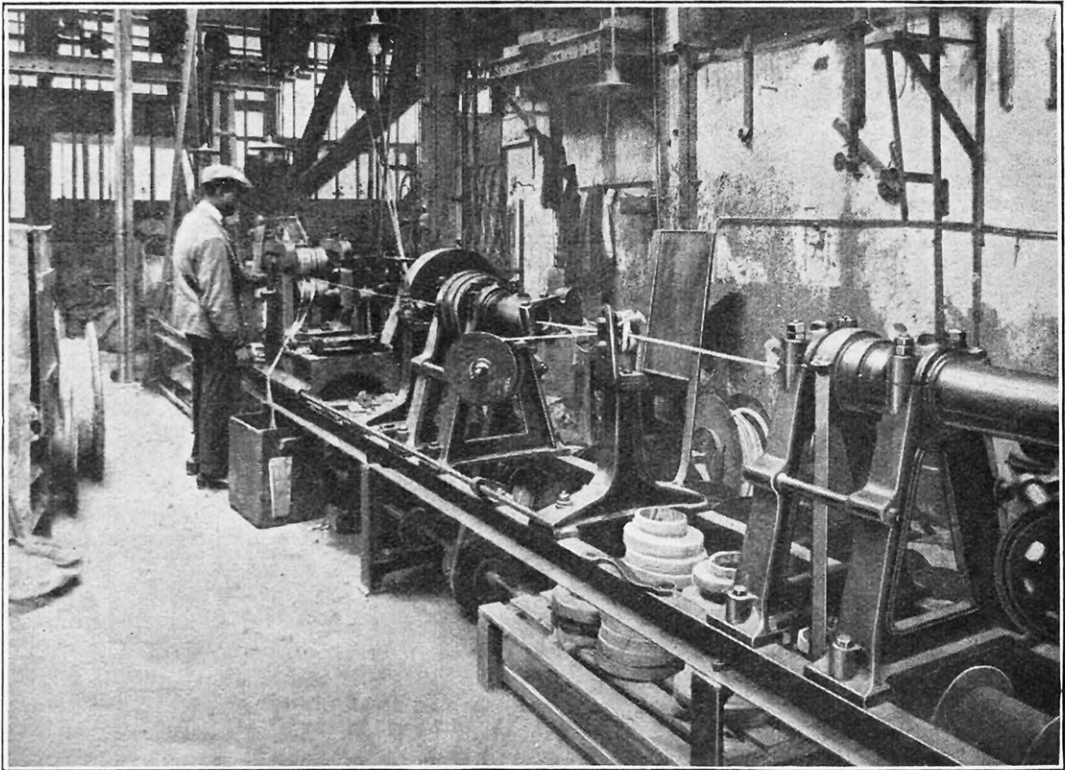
MACHINE A GALETS POUR GROS CABLES, ISOLANT UN SEUL CABLE PAR LA SOUDURE DES BANDES DE CAOUTCHOUC
